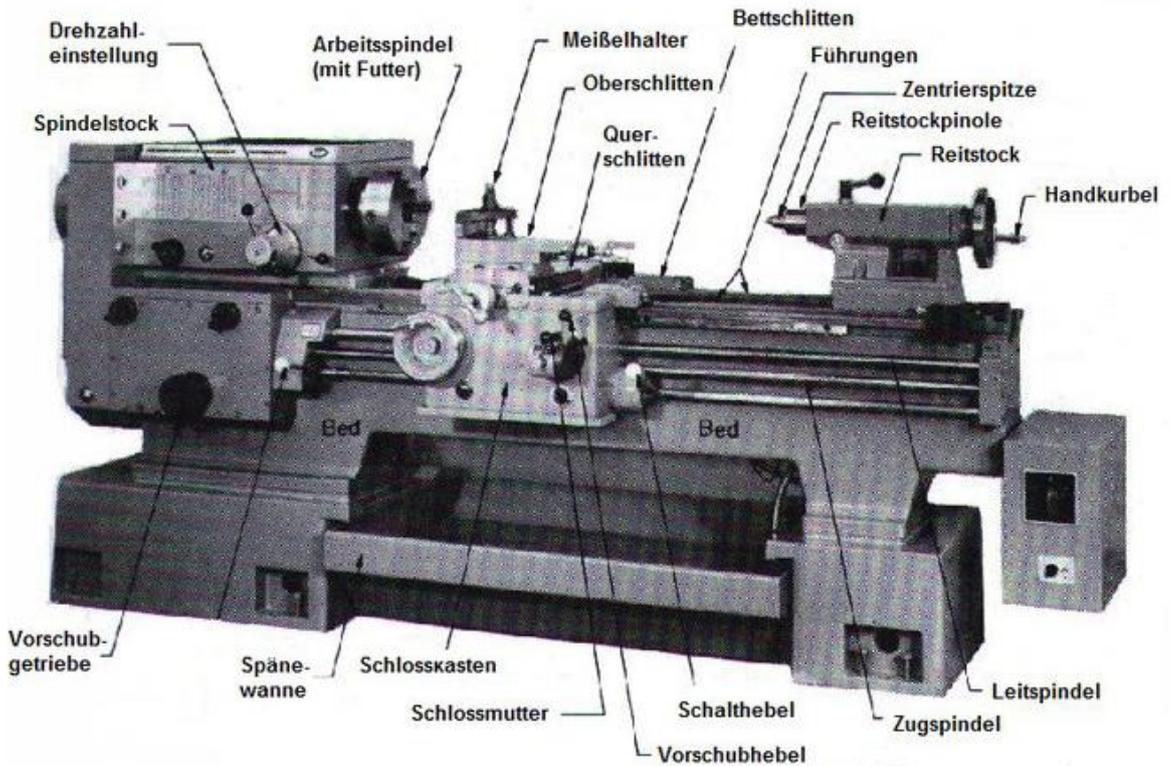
Aufbau einer konventionellen Drehmaschine [Fach1998]
